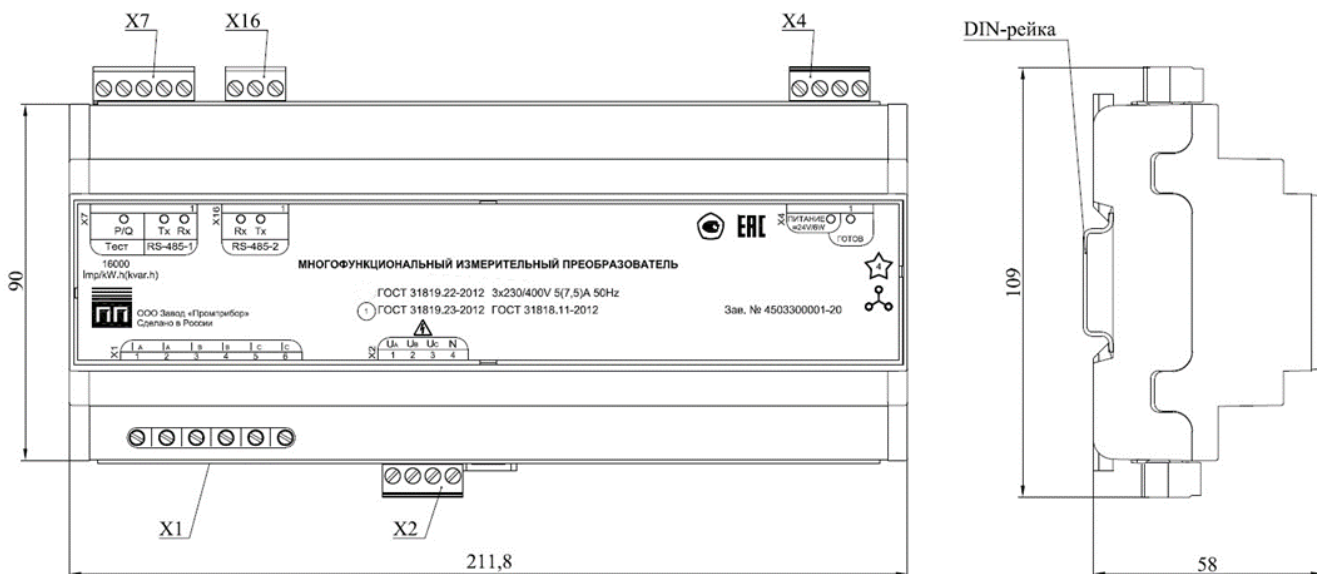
Внешний вид и габаритные размеры МИП
